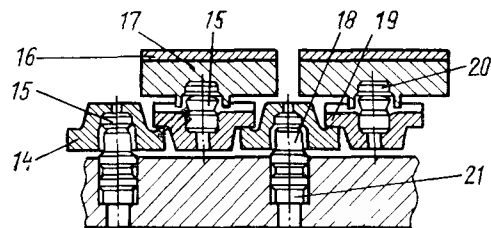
Упорный подшипник конструкции ХТГЗ:
